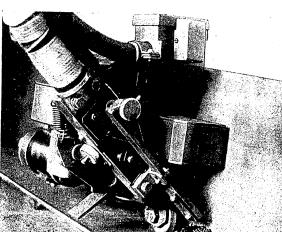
Автоматическая сварочная головка ГСА-2-2 для сварки угловых швов
